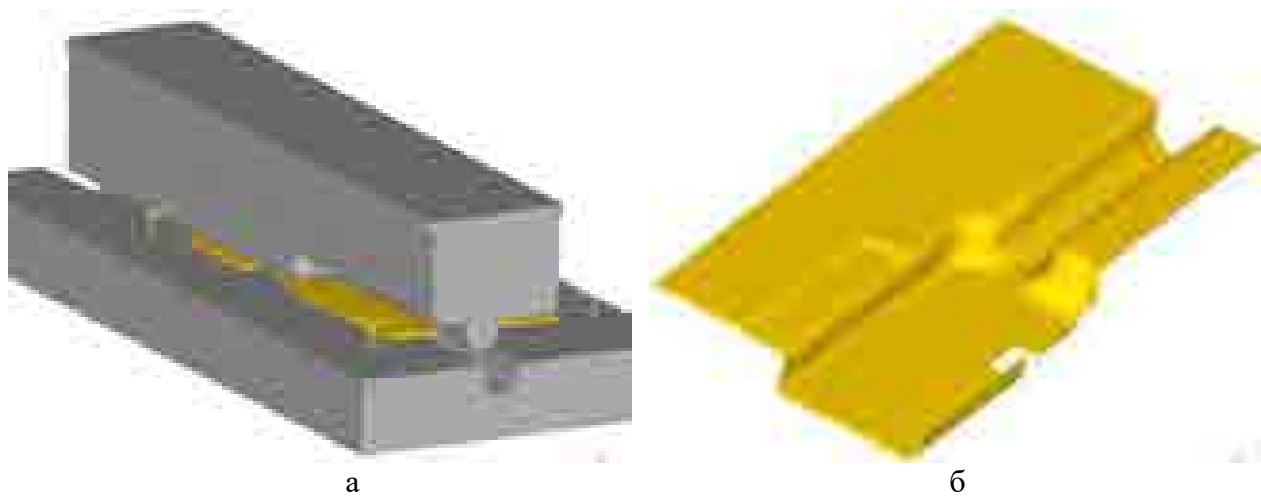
Моделювання деформування заготовки з початковою геометрією:
